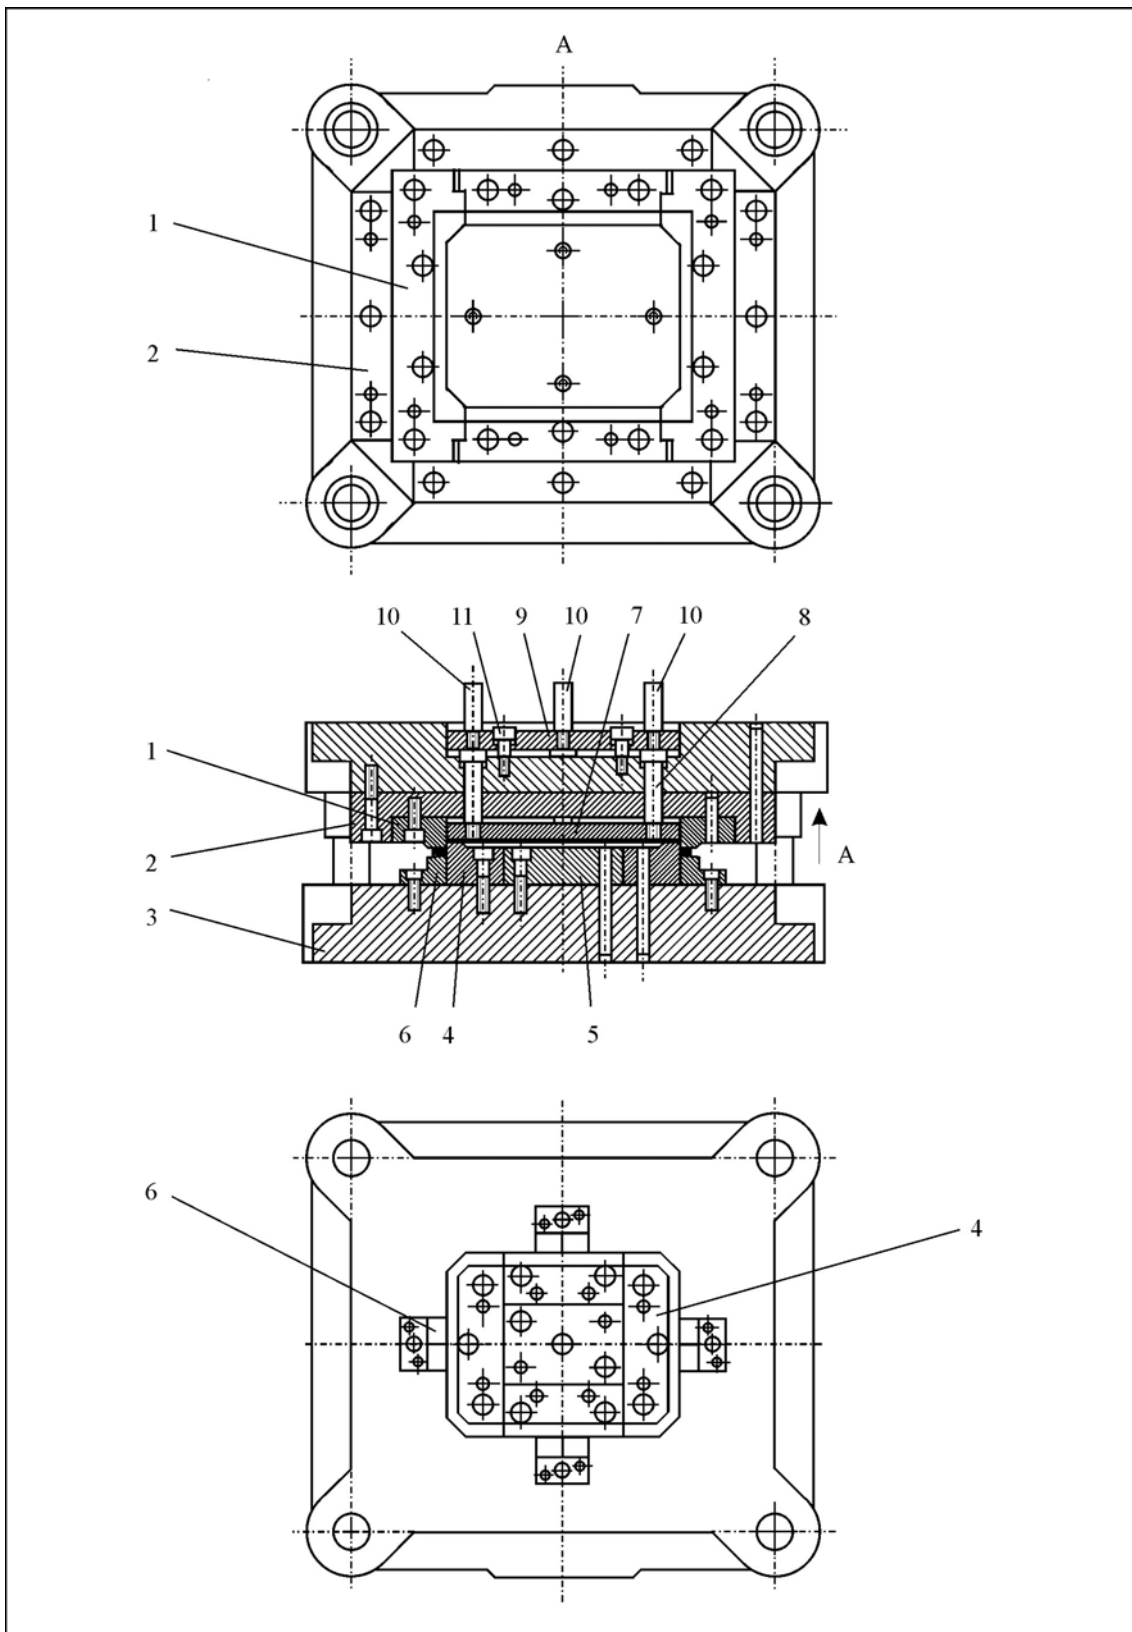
Штамп для вирубвання великогабаритної деталі: 1 – секційна матриця; 2 – обойма; 3 – нижня плита; 4 – секційний пуансон; 5 – базова планка; 6 – ніж; 7 – виштовхувач; 8 – штовхач; 9 – траверса; 10 – штовхачі
